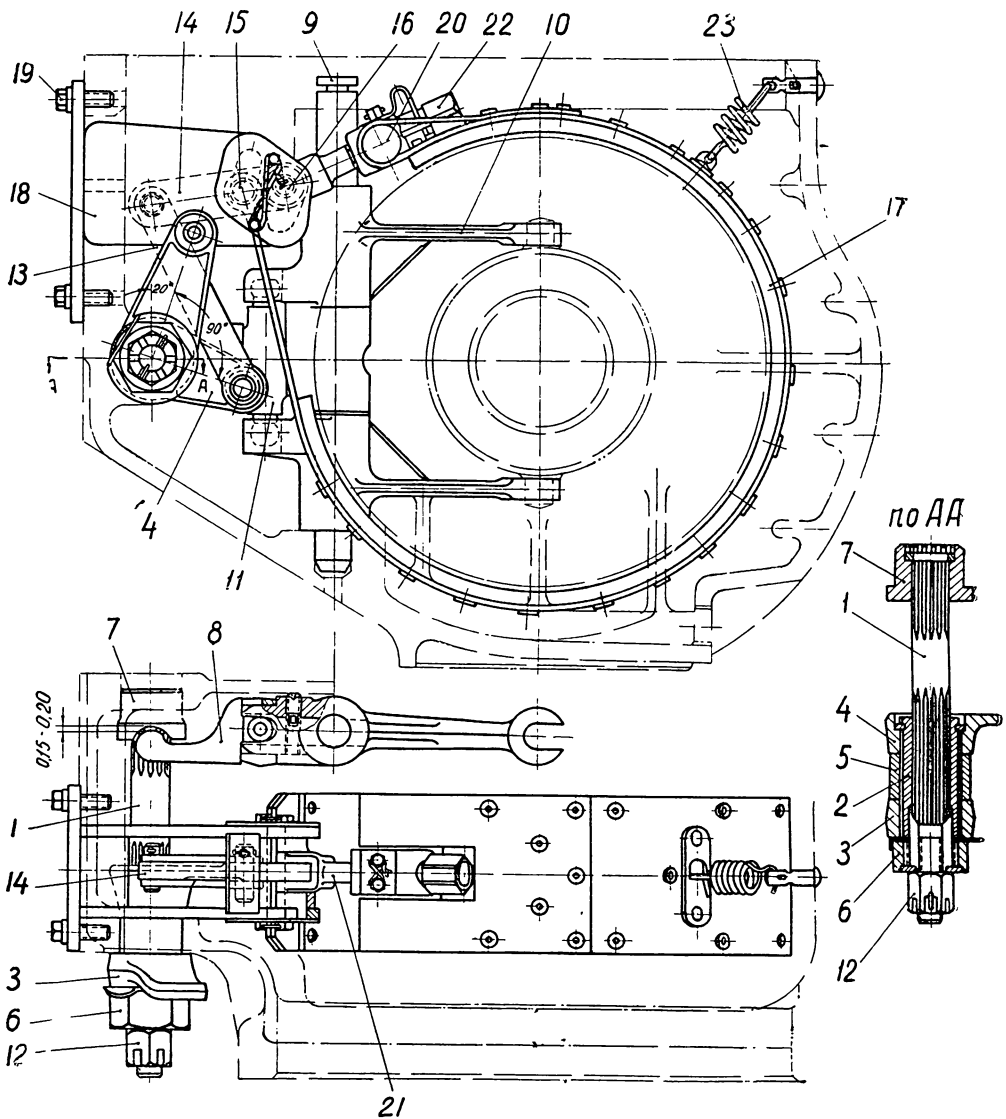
Тормоз и механизм управления муфтами поворота и тормозом:
